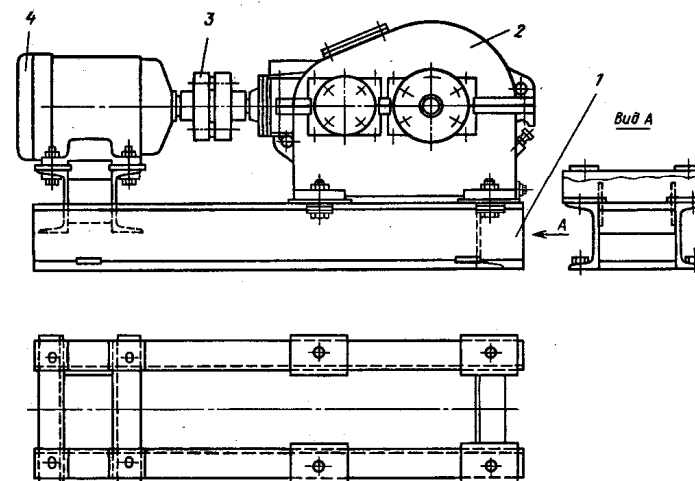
Установка привода на сварной раме из швеллеров:
